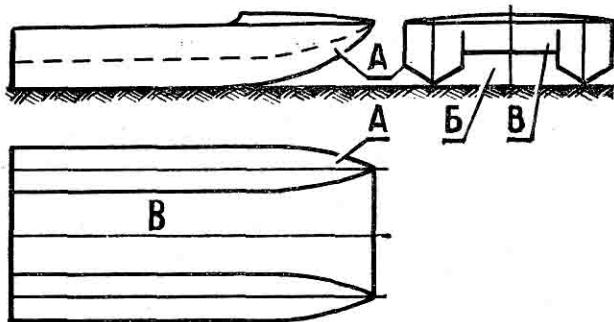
Катамаран: А — корпуса, Б — тоннель, В — соединяющий корпуса мостик.
